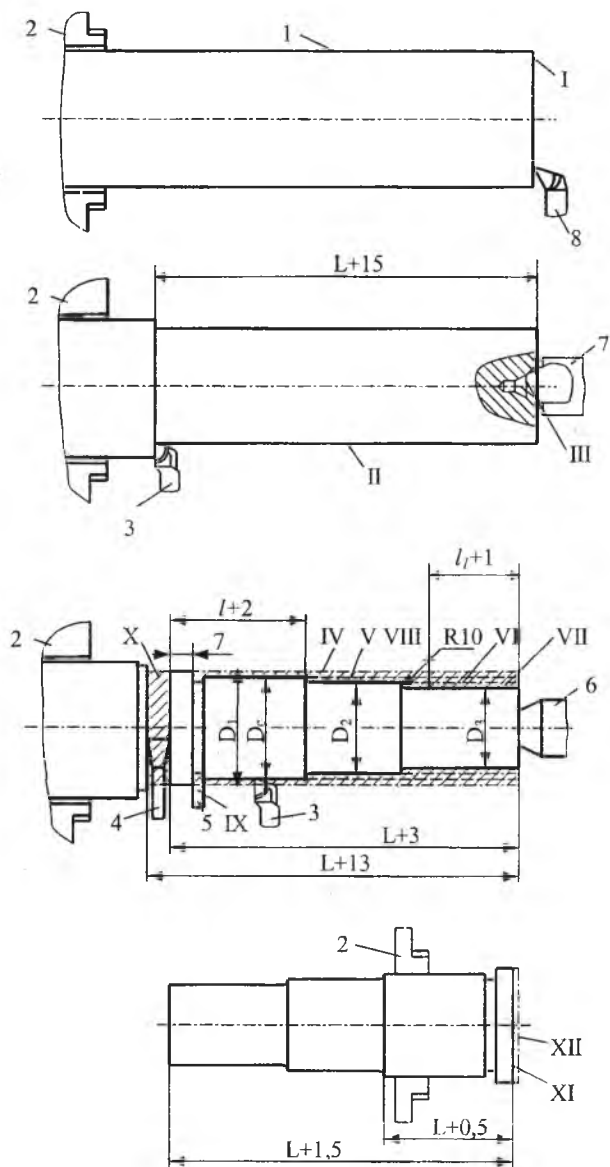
Обработка пуансона с заплечиком: 1 – заготовка; 2 – патрон; 3 – проходной резец; 4 – отрезной резец; 5 – канавочный резец; 6 – вращающийся центр; 7 – центровочное сверло; подрезной резец
